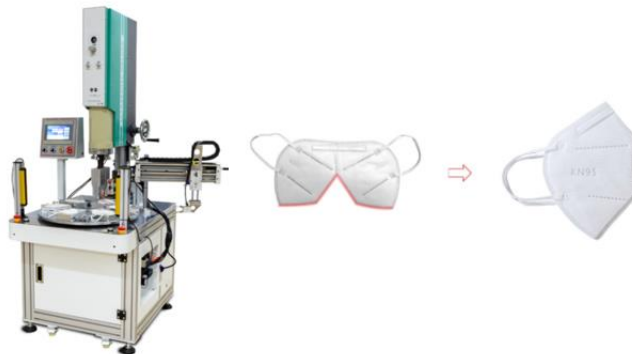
Máquina de soldadura ultrasónica de borde de máscara (Fuente: www.testertextile.com)
